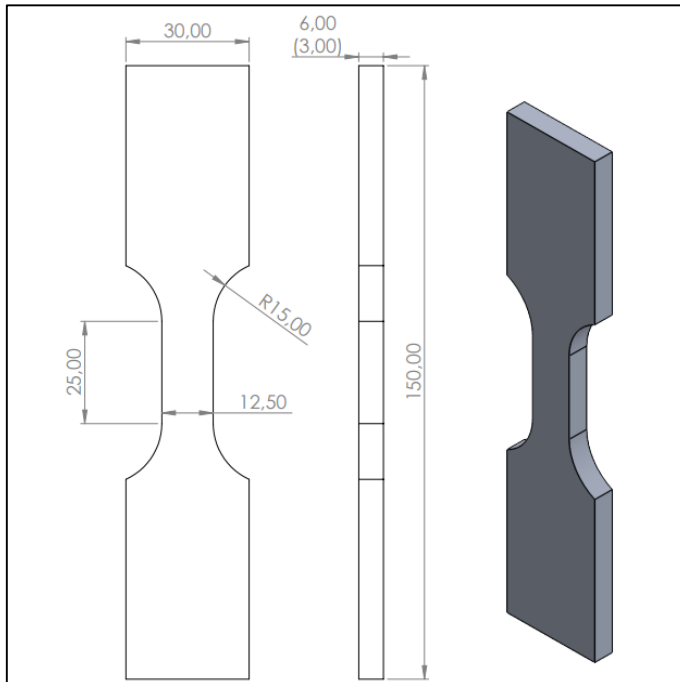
Desenho técnico do corpo de prova para a chapa de espessura 1,50 mm com dimensões definidas conforme a norma ABNT NBR 6892
